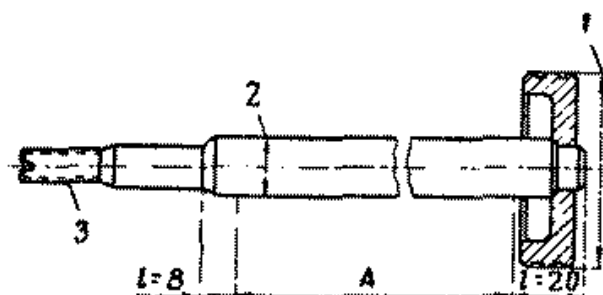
Поршень цилиндра гидроусилителя руля со штоком в сборе
